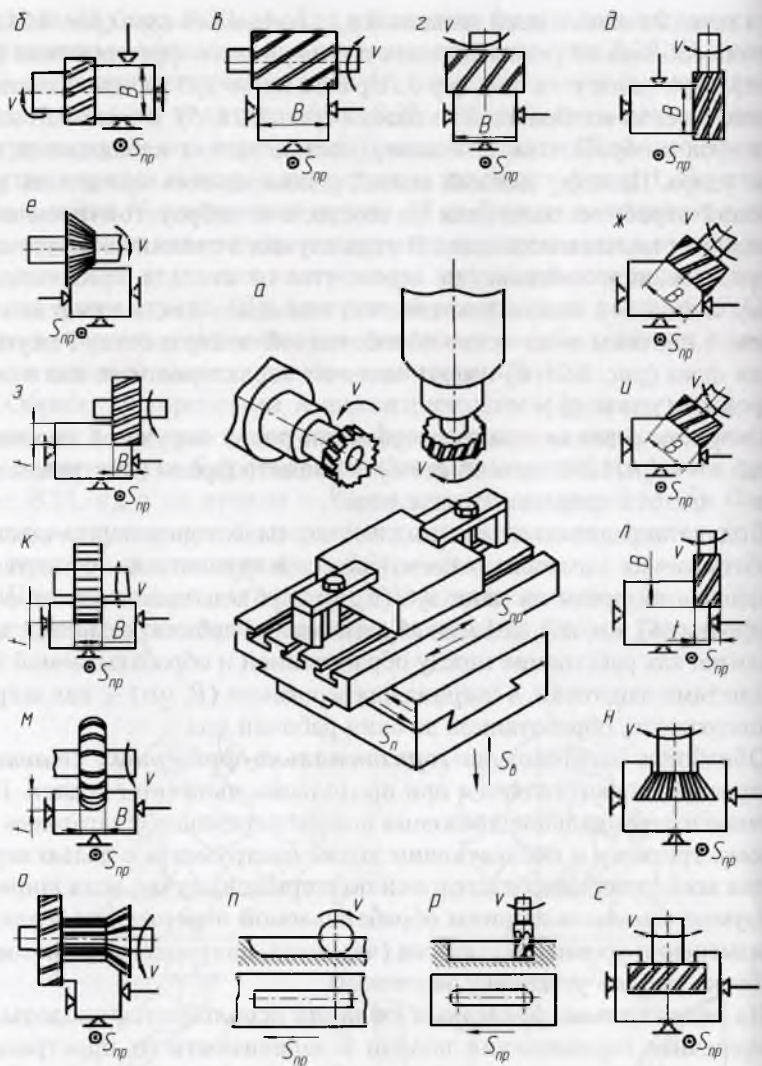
Схемы фрезерования поверхностей на горизонтально- и вертикально-фрезерных станках:
